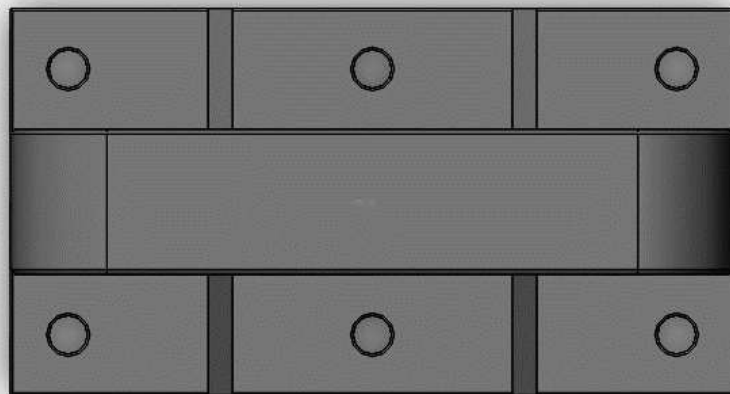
Крепление для двигателя (вид сверху)
